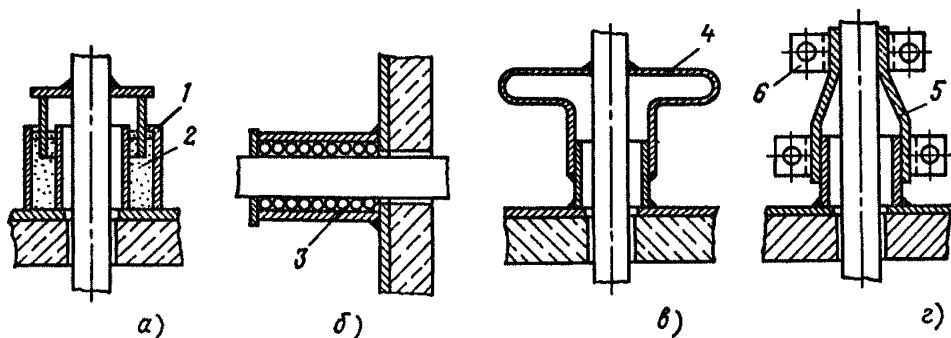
Конструкции уплотнений прохода через обшивки котла.
